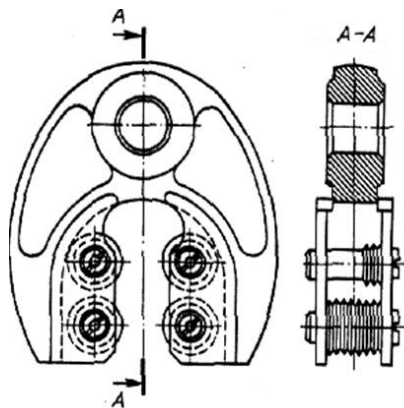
Резьбовой калибр – скоба с твердосплавными рабочими элементами
